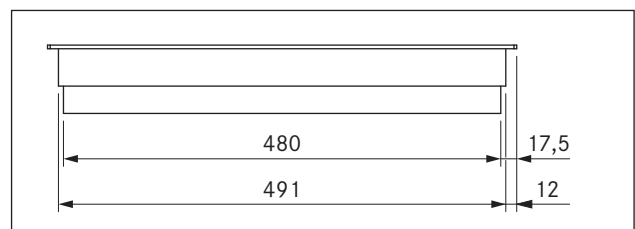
CKCB apparatets dimensjoner sett fra siden
